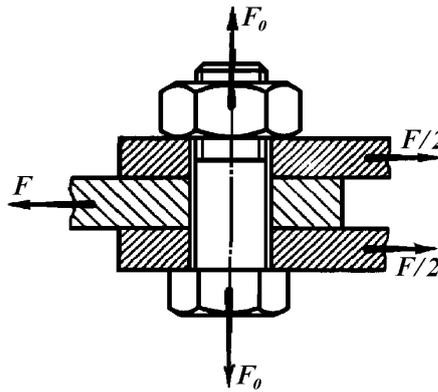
Болтовое соединение, нагруженное поперечной силой.
